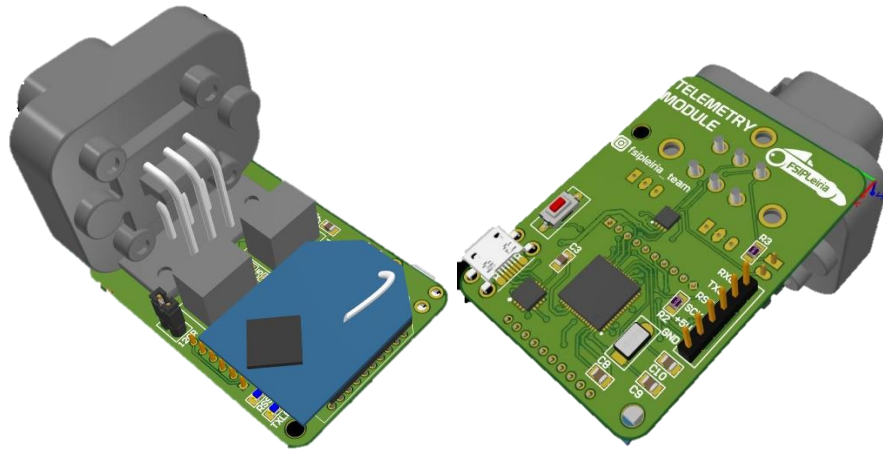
Design Final da PCB do Módulo da Telemetria - 3D
